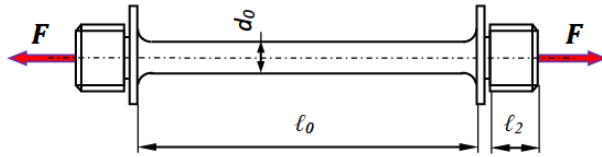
Ескіз зразка для випробувань на ударний розтяг.
